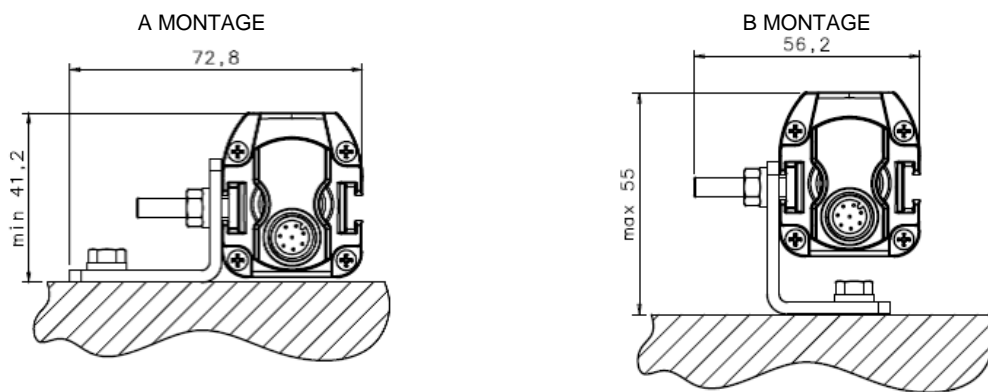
Abmessungen Montagewinkel mit Profil
